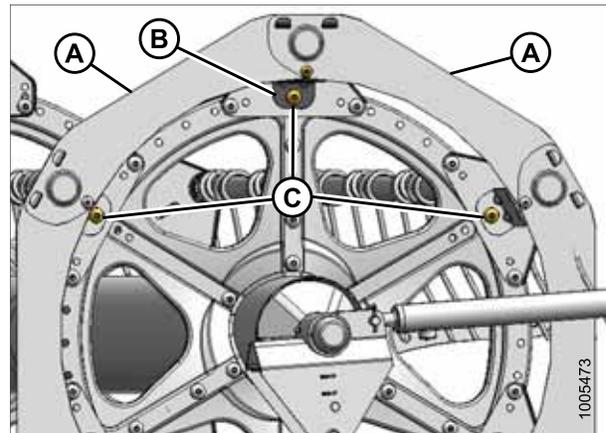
Опоры боковых щитков подбирающего мотовила
